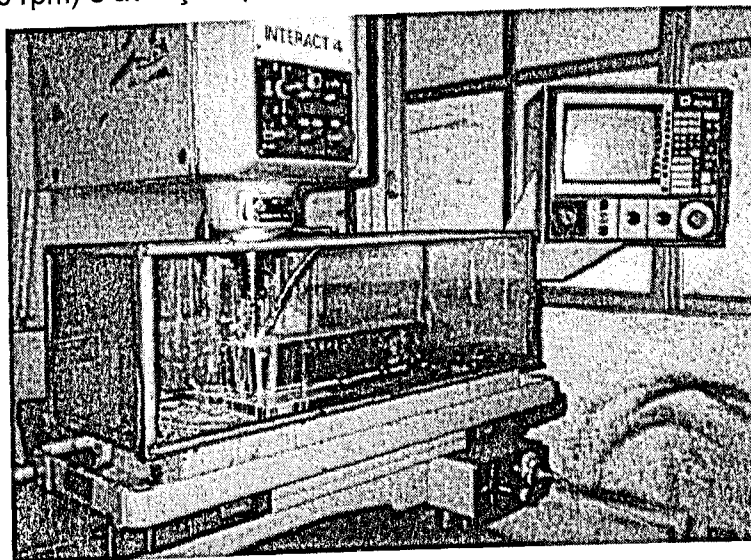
Fresadora CNC utilizada nos ensaios
